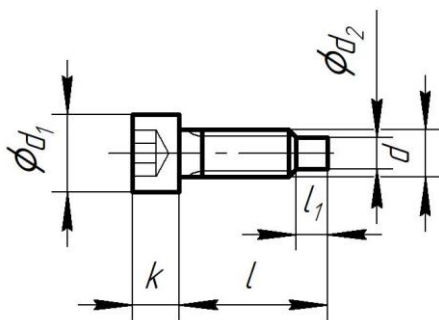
Установочный винт с цилиндрической головкой и шестигранным углублением под ключ для эксцентриковых пальцев
